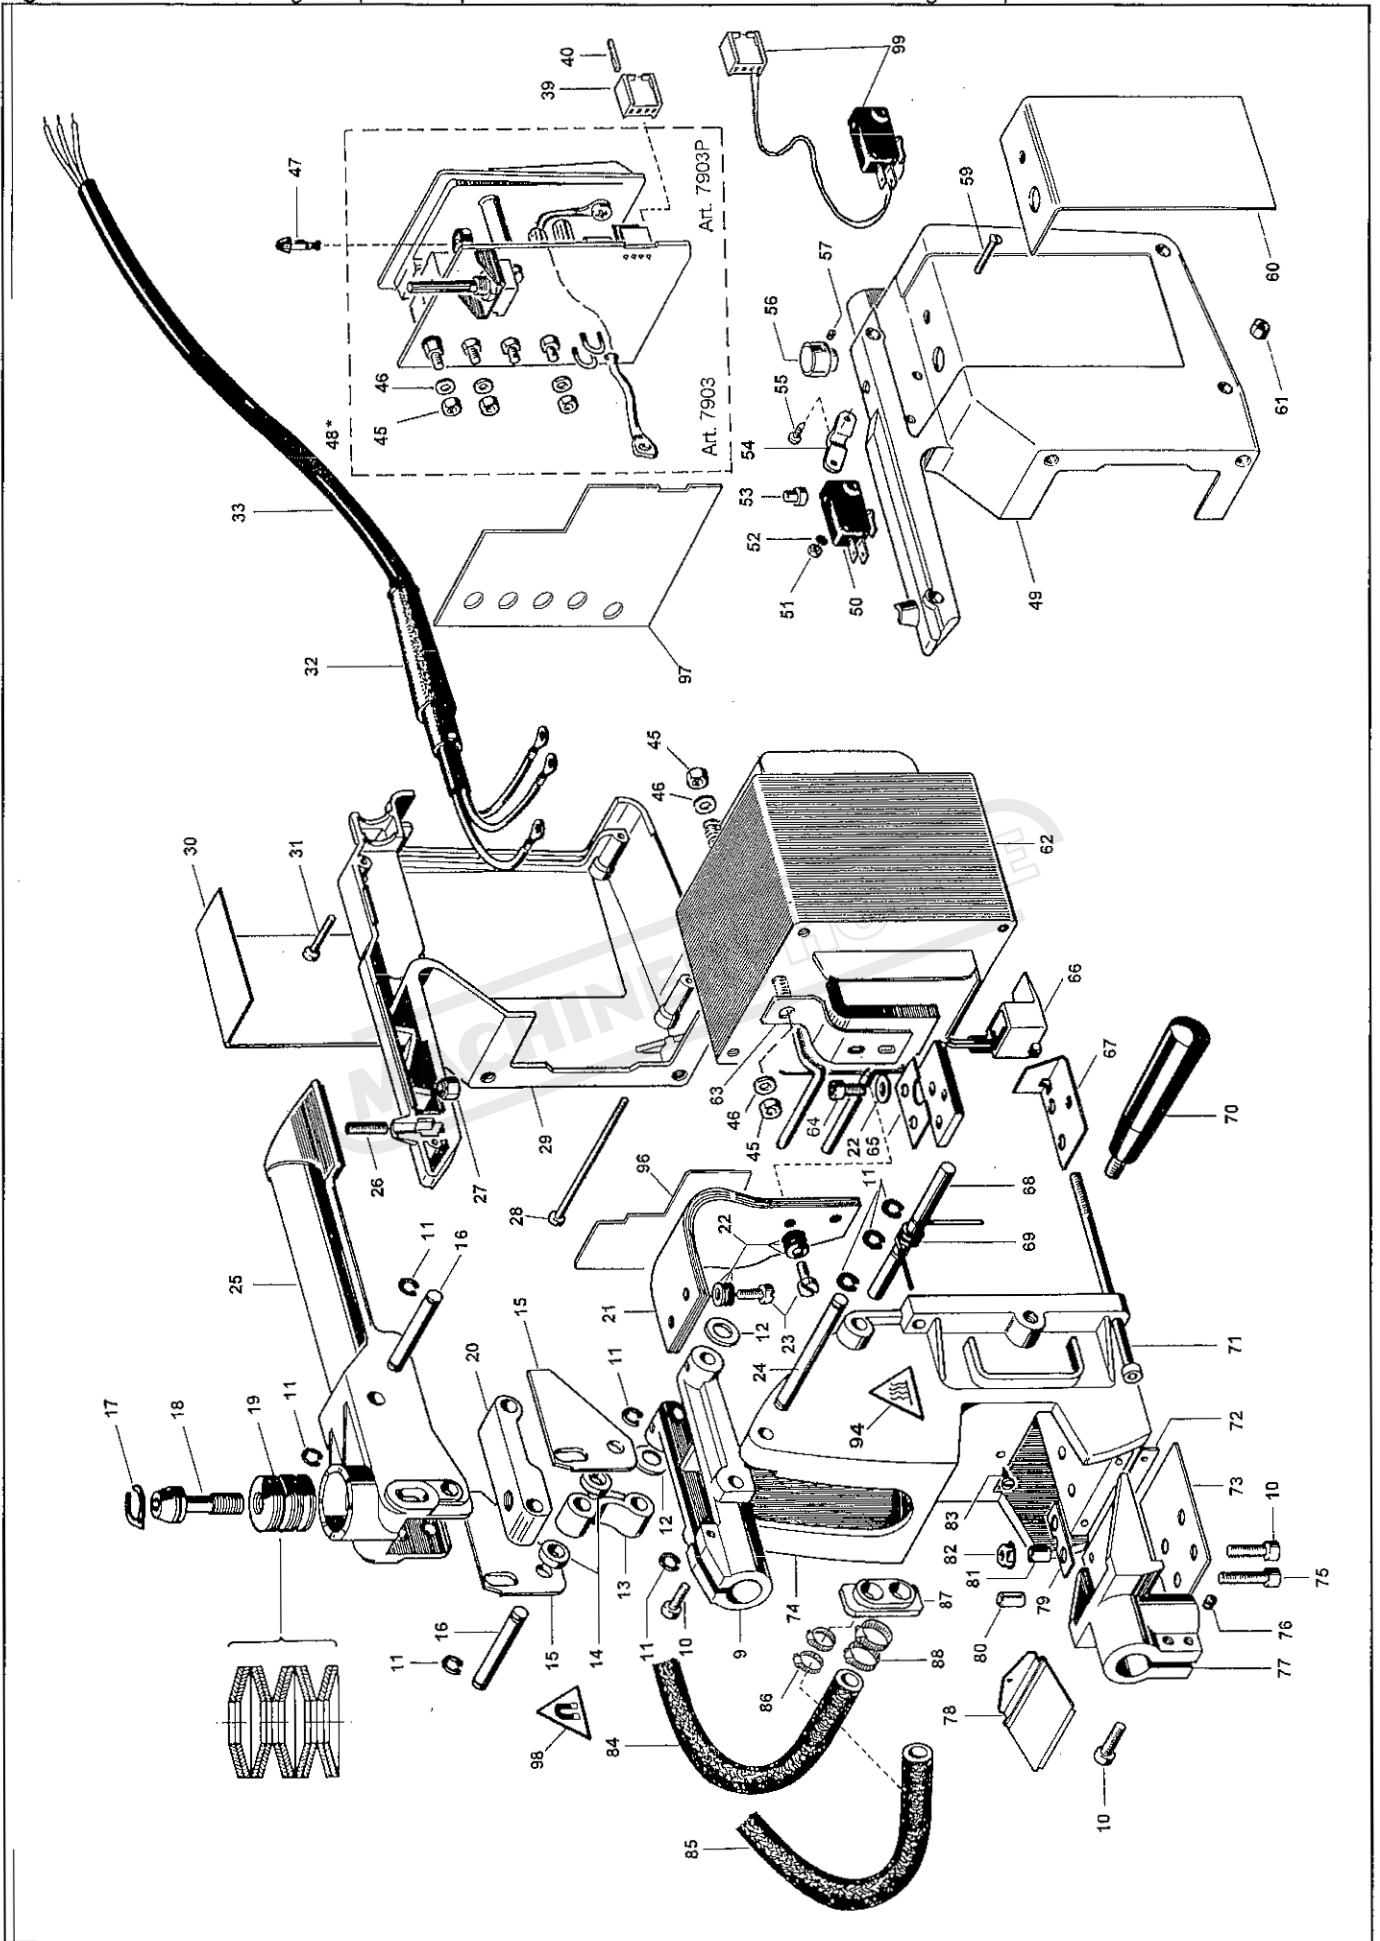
Art./Item 7903 Disegno esploso - Exploded view - Vue éclatée - Ersatzteilzeichnung - Croquis
